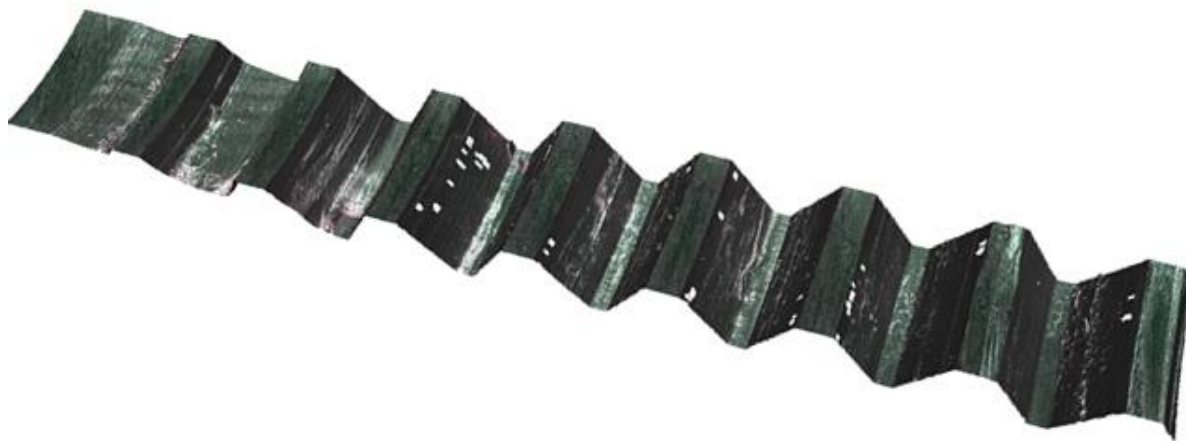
Profil závitu s vyznačenou horní mezní tolerance H7
